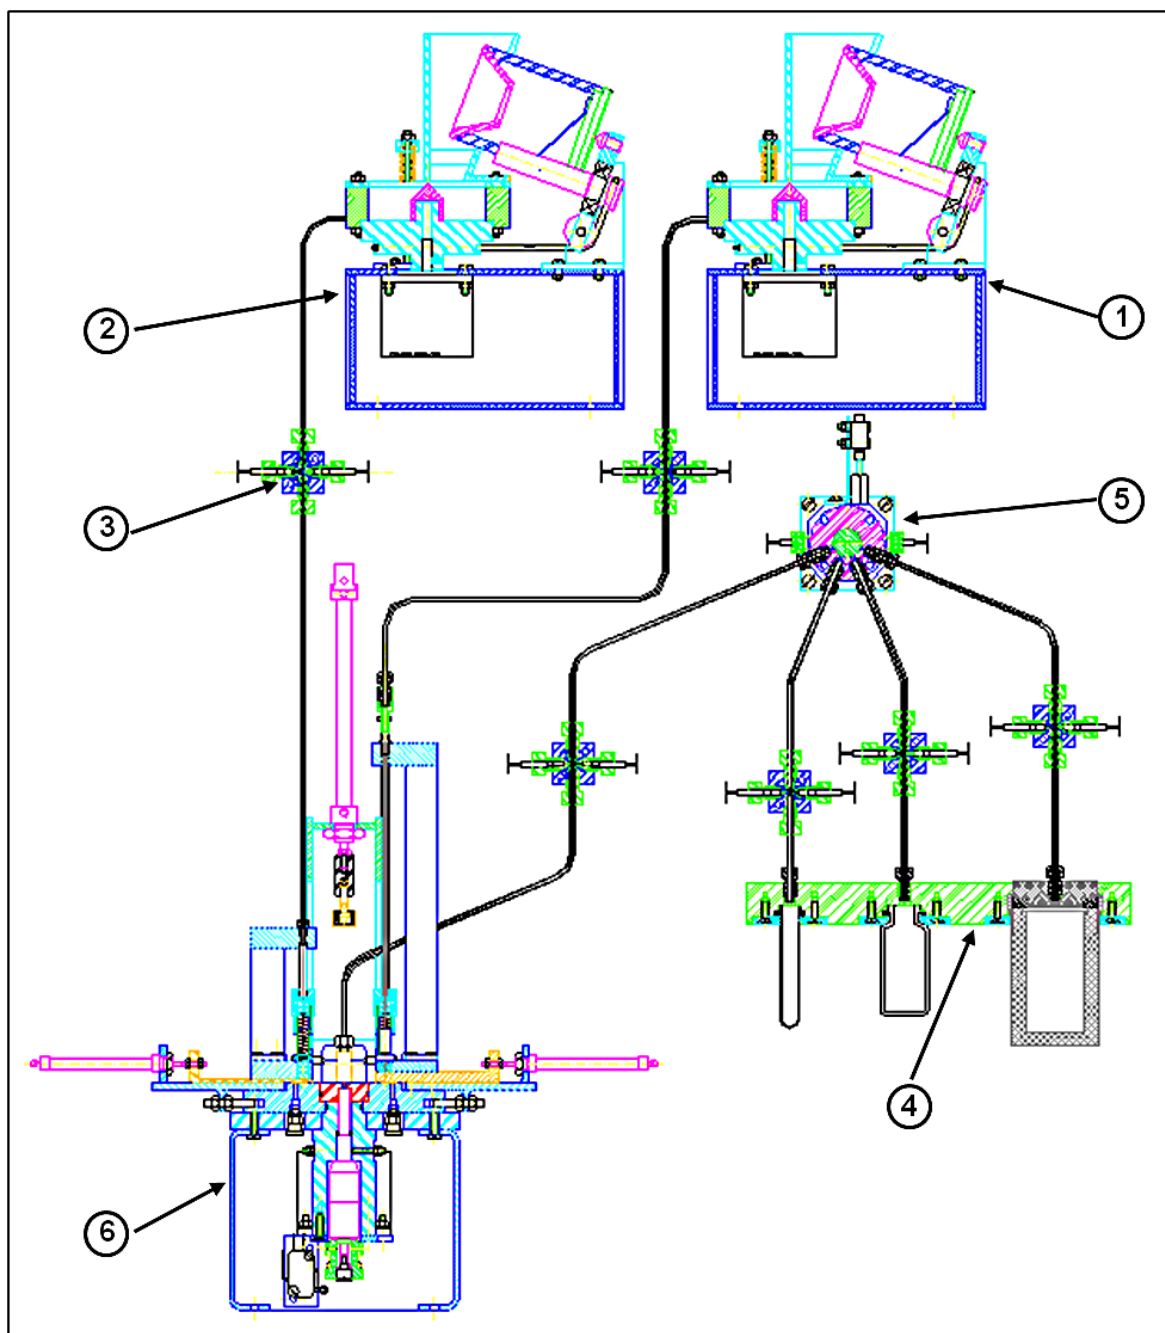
Sistema de soldagem a laser constituído por: seletor e alimentador de cânulas (1), seletor e alimentador de fontes (2), suporte para sensor em fibra óptica (3), receptor de fontes seladas (4), distribuidor inversor (5) e dispositivo de soldagem (6)
